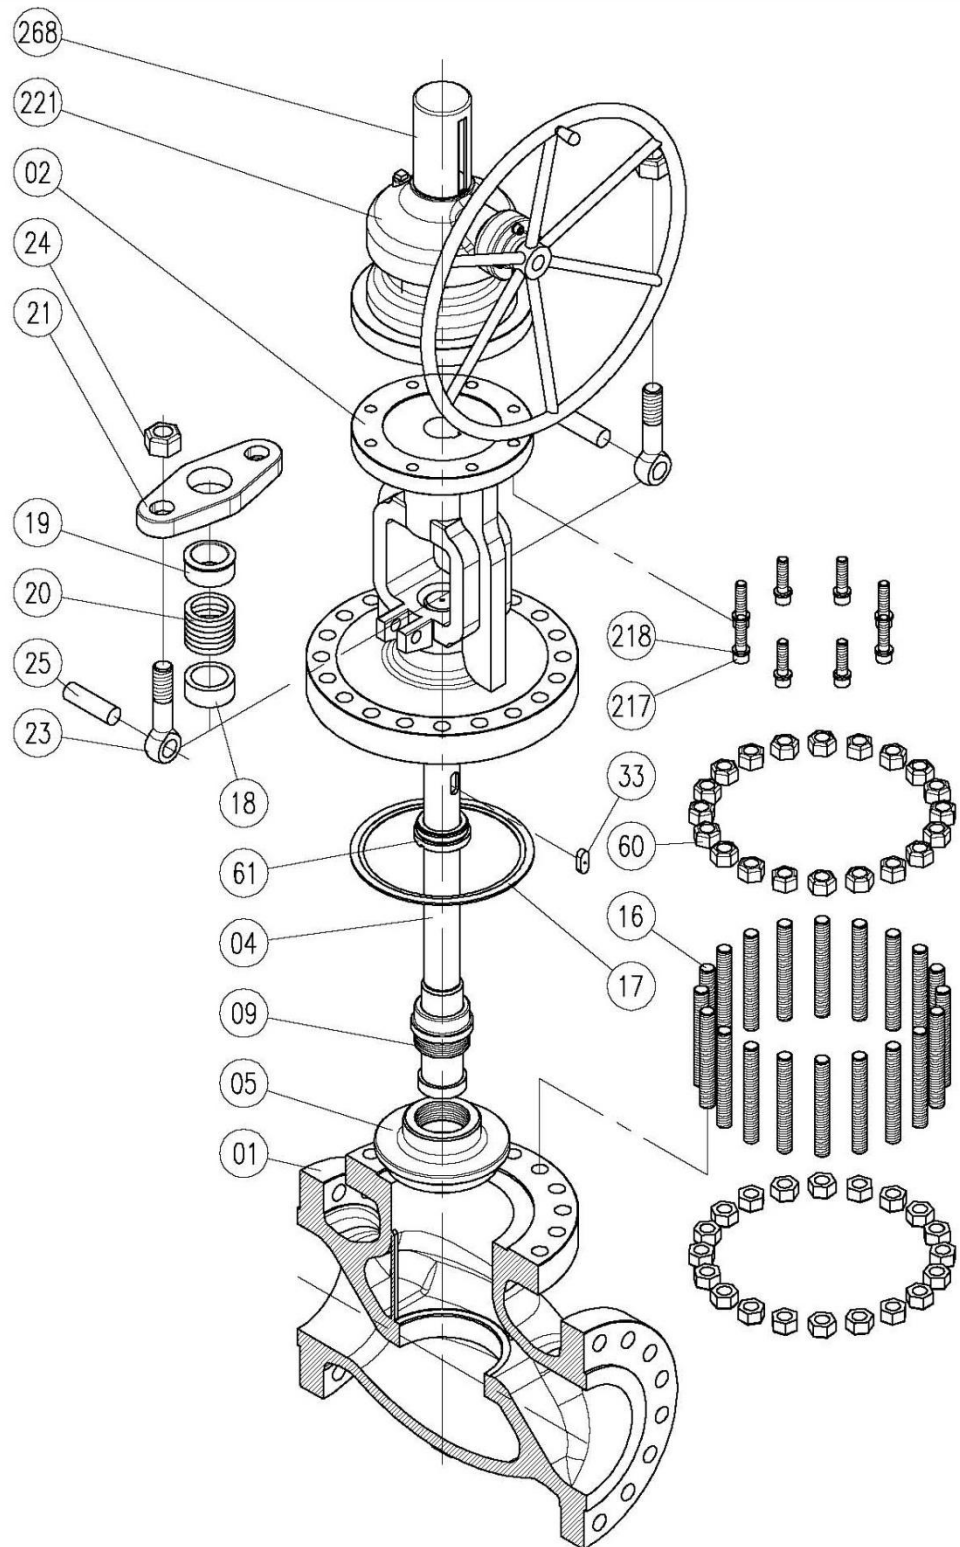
BOLTED BONNET GLOBE 밸브 분해도
